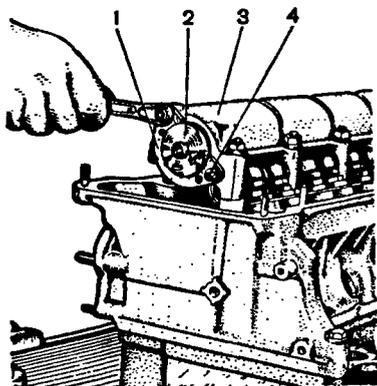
Снятие упорного фланца распределительного вала: 1 - упорный фланец; 2 - распределительный вал; 3 - корпус подшипников; 4 - шпилька крепления упорного фланца
